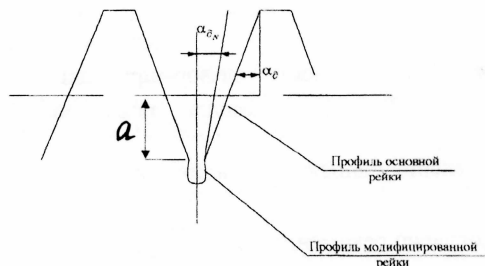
Профиль червячной фрезы с модифицированным производящим контуром (с протуберанцем) для чистового зубофрезерования.
